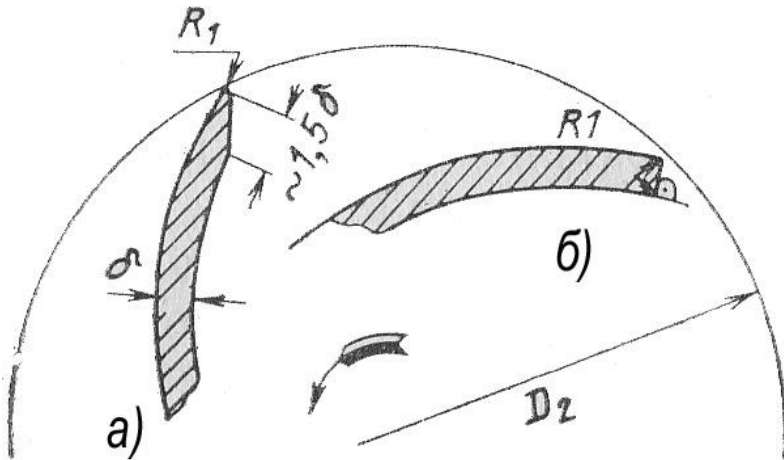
Підрізання тильного боку лопаті робочого колеса:
